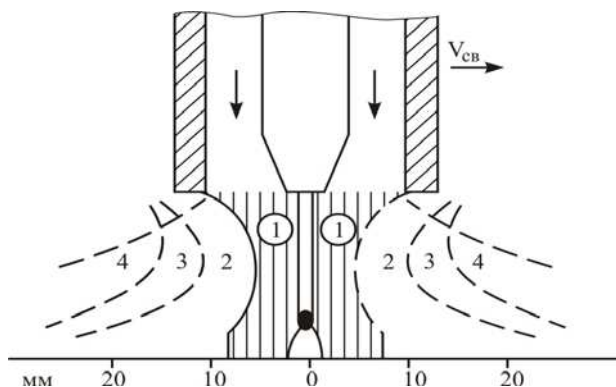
Состав струи углекислого газа, истекающего из сопла сварочной горелки: 1 – 100 % CO₂; 2 – CO₂ + 10 % воздуха; 3 – CO₂ + 60 % воздуха; 4 – CO₂ + 80 % воздуха
